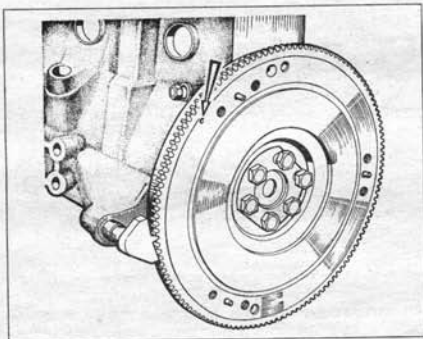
Блокировка маховика фиксатором 67.7820.9526. Стрелкой показана метка в.м.т. поршней 1- и 4-го цилиндров.
